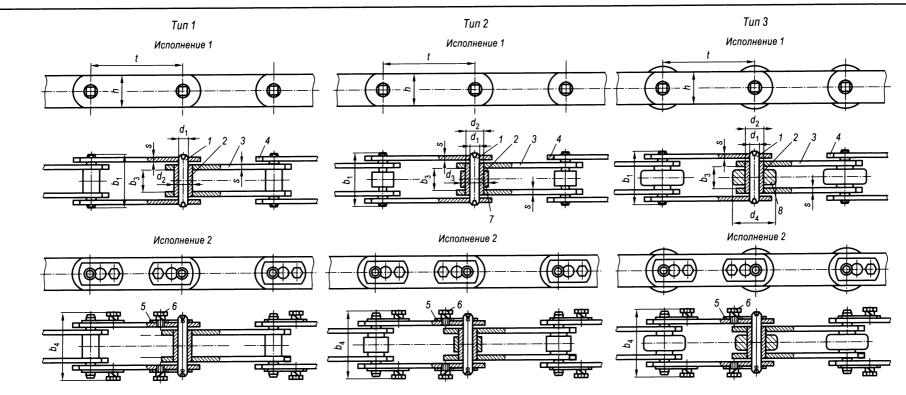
Втулочная (*тип 1*), роликовая (*тип 2*) и катковая с гладкими катками (*тип 3*) тяговые пластинчатые цепи: 1 – валик; 2 – втулка; 3 – внутренняя пластина; 4 – наружная пластина; 5 – ригель; 6 – винт; 7 – ролик; 8 – каток
